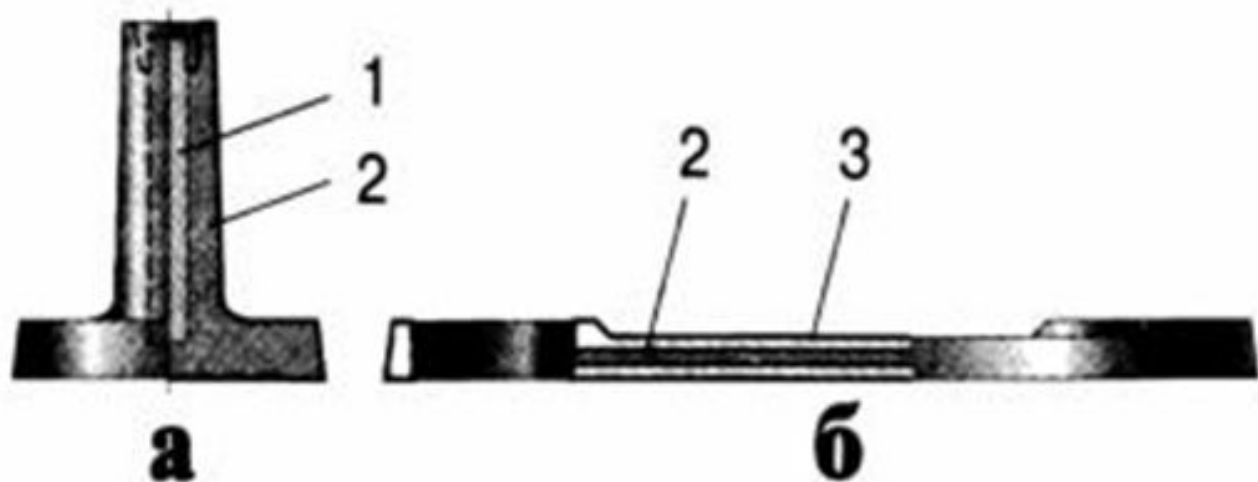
Токоведущие детали батареи с медными вкладышами:
